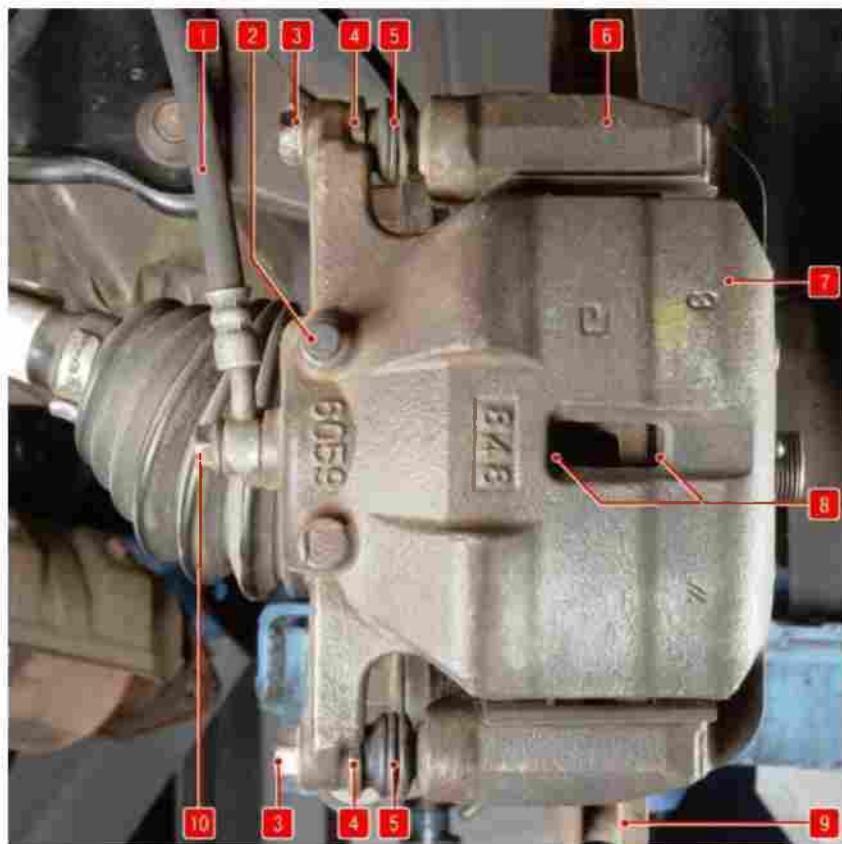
Тормозной механизм переднего колеса: 1 – тормозной шланг; 2 – клапан выпуска воздуха; 3 – болт крепления направляющего пальца суппорта; 4 – направляющий палец суппорта; 5 – пыльник направляющего пальца; 6 – направляющая колодок; 7 – суппорт тормозного механизма; 8 – тормозные колодки; 9 – тормозной диск; 10 – болт штуцера тормозного шланга.
